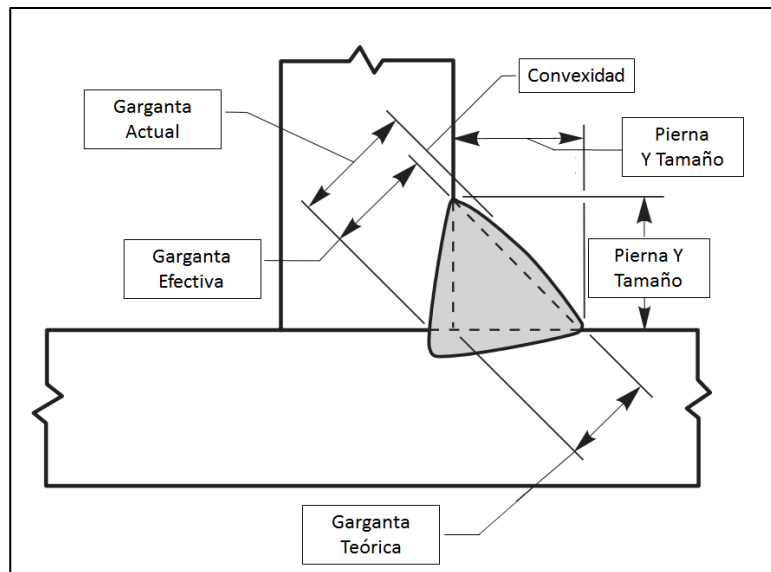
Soldadura De Filete Convexa [11].
